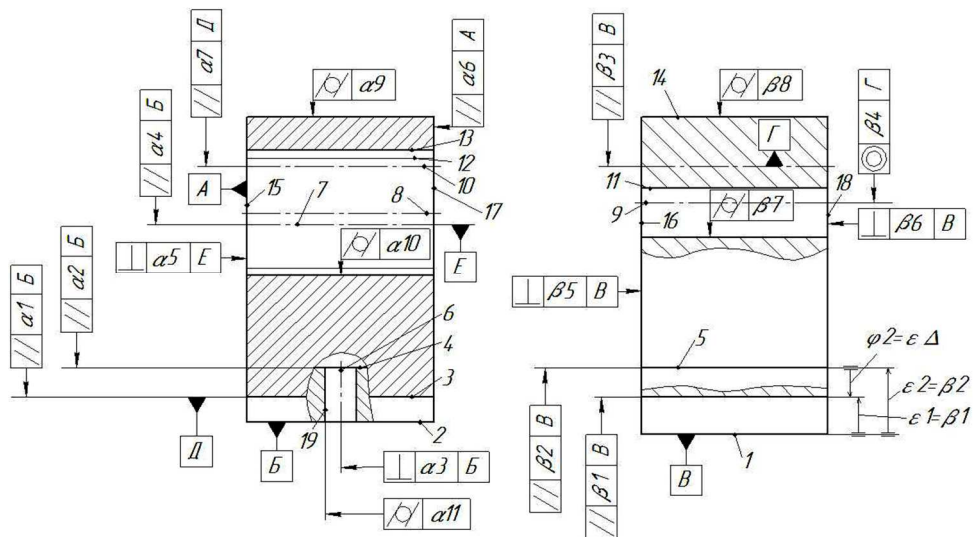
Совмещенный эскиз детали и заготовки (плоскость YZ)
